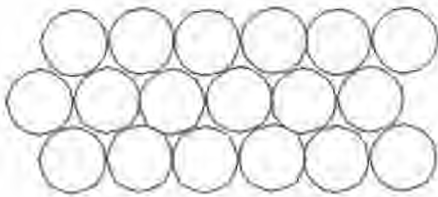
DEPOSICIÓN DE MATERIAL EN EL PROCESO FDM
